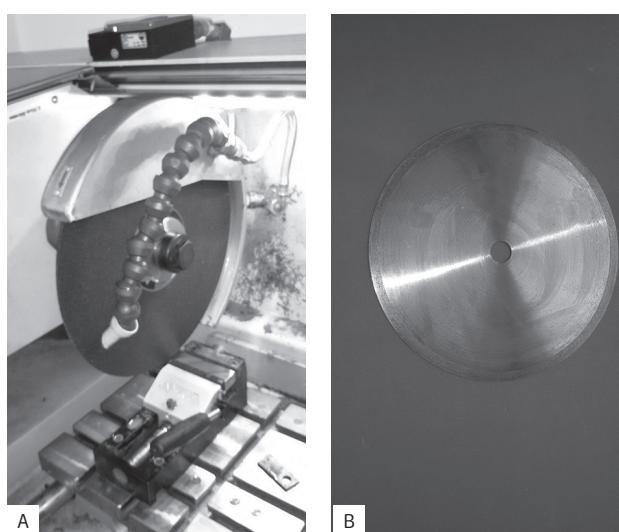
(a) Discos de corte grosso posicionado na máquina. (b) Disco de corte fino.
